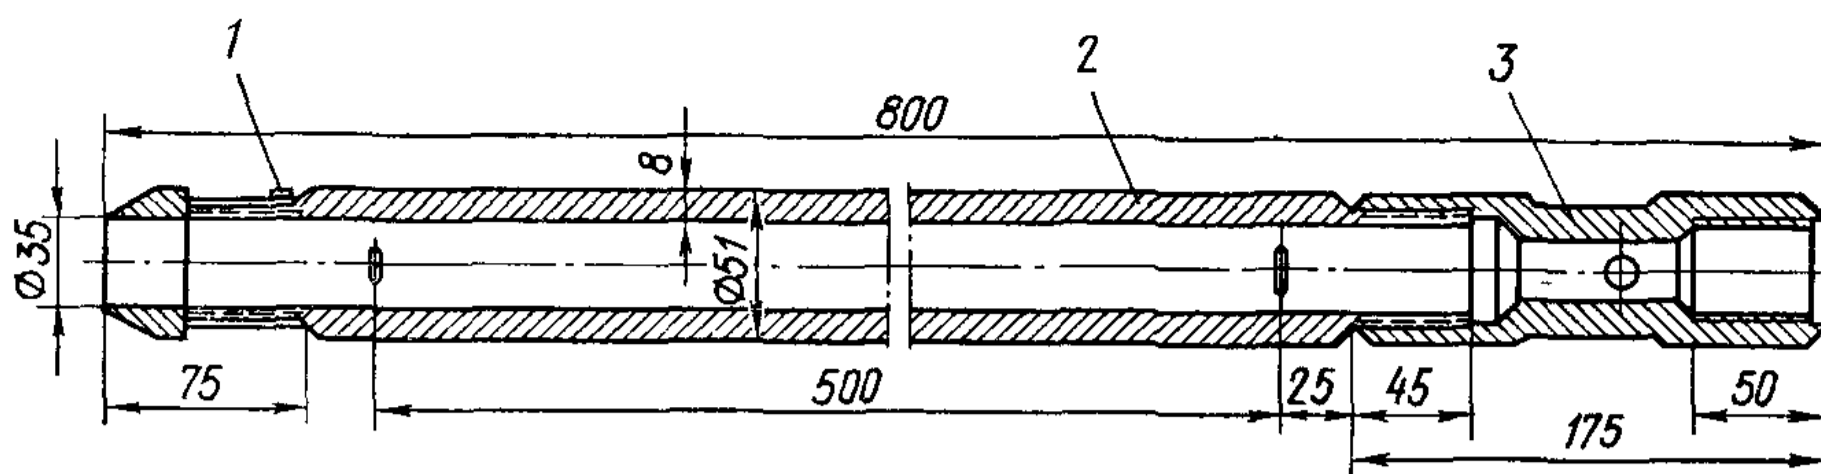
Пробоотборник Фундаментпроекта для испытания грунтов динамическим зондированием:
